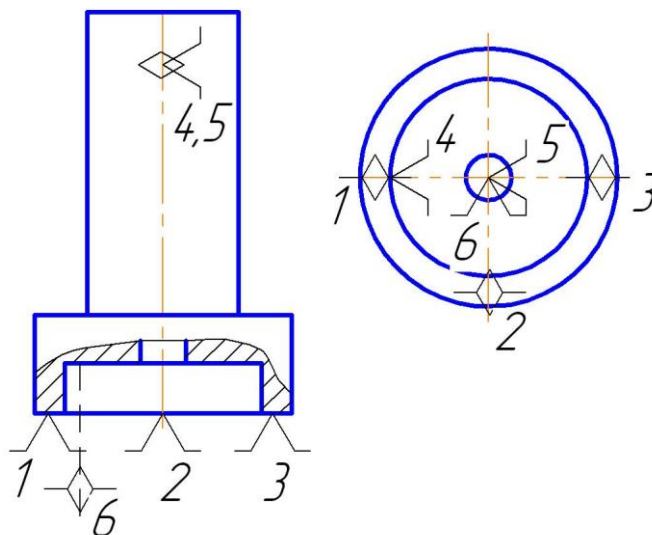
Теоретична схема базування при фрезерування зуб'їв на вертикально-фрезерному напівавтоматі
